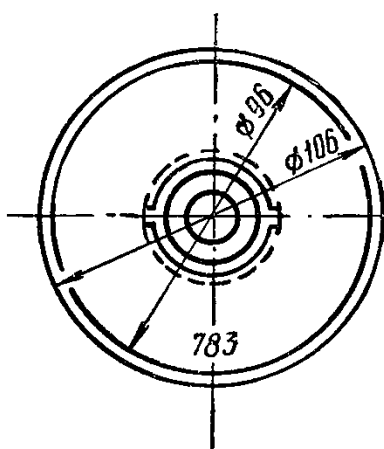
Штанговый стенной знак конструкции Б. К. Корнева
